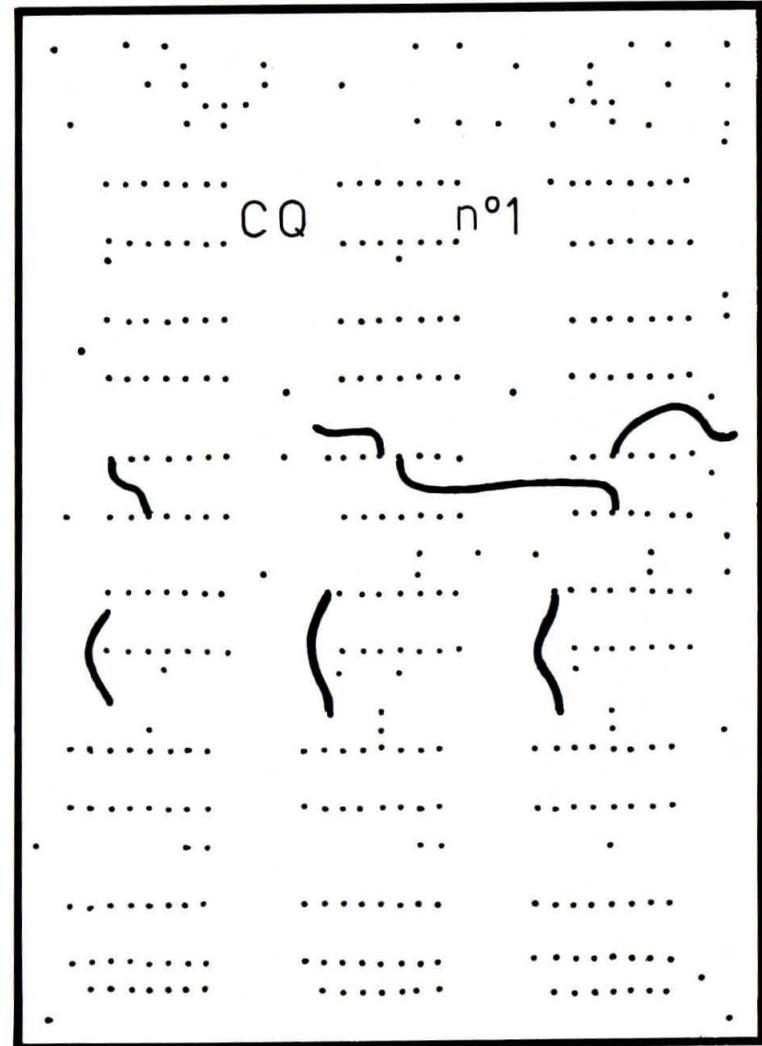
Dibujo de los puentes que hay que hacer por el lado de las pistas de cobre.
